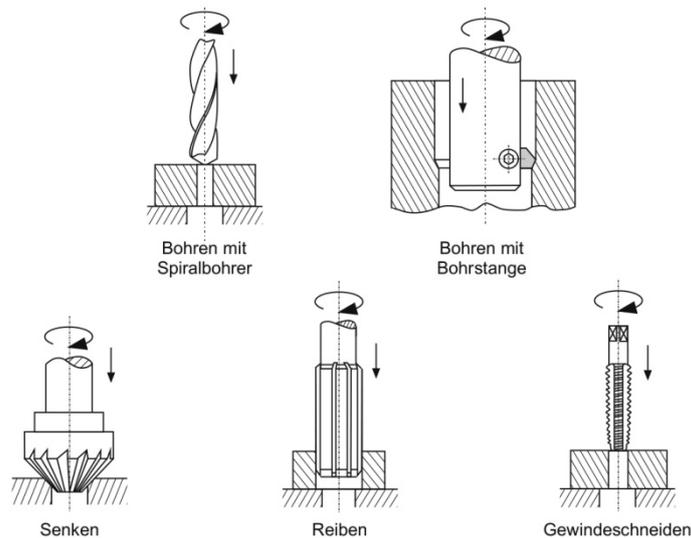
Mit Bohrmaschinen durchführbare Bearbeitungsarten; Quelle: Werkzeugmaschinen - Maschinenarten und Anwendungsbereiche, Springer
